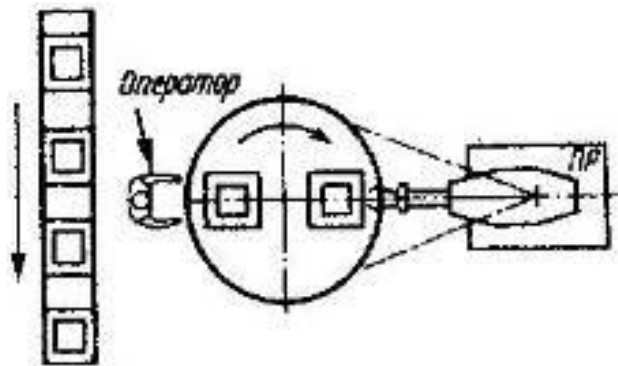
Робот для зварювання й поворотний стіл
